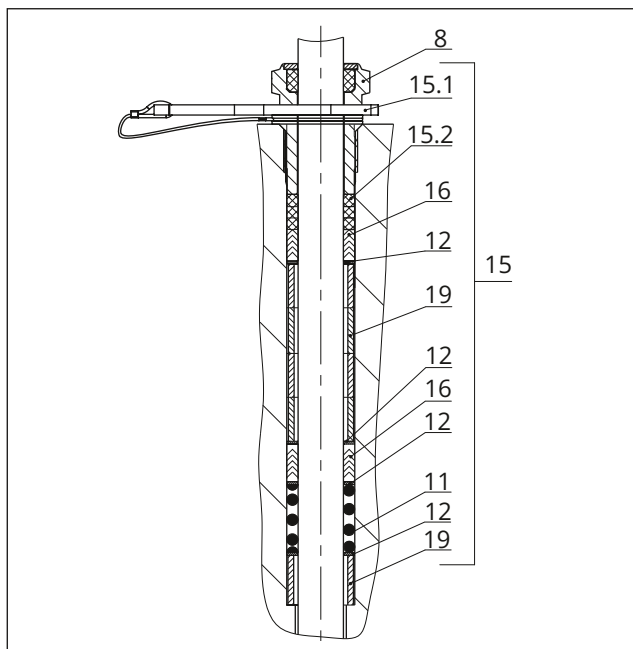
Empaquetadura ADSEAL: DN 50...100/NPS 2...4
